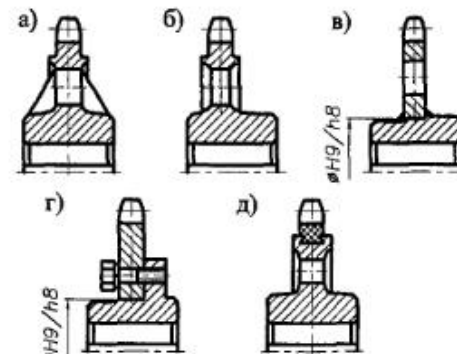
Конструкции звездочек: а) литая с ребрами; б) дисковая; в) сварная; г) составная; д) венец и ступица из различных материалов
